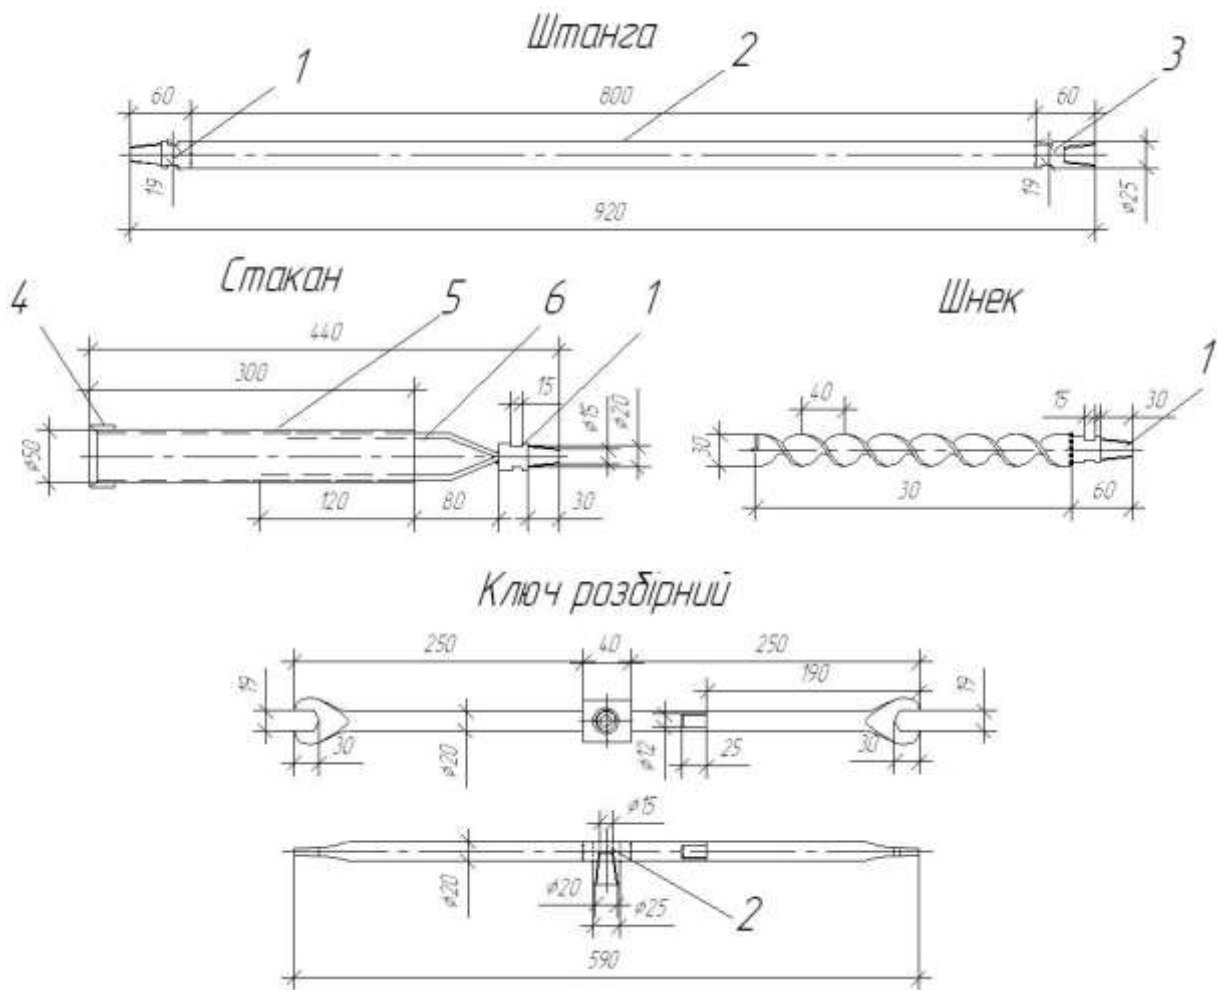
Ручний буровий комплект: 1 – приварна деталь із зовнішньою конічною різзю; 2 – труба ДУ-25; 3 – приварна деталь із внутрішньою конічною різзю; 4 – приварне кільце із внутрішнім діаметром 50 мм; 5 – труба ДУ-25; 6 – металева штаба
